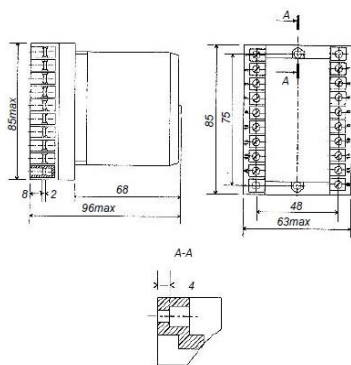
Габаритные и установочные размеры реле промежуточного РПУ-2М-211
